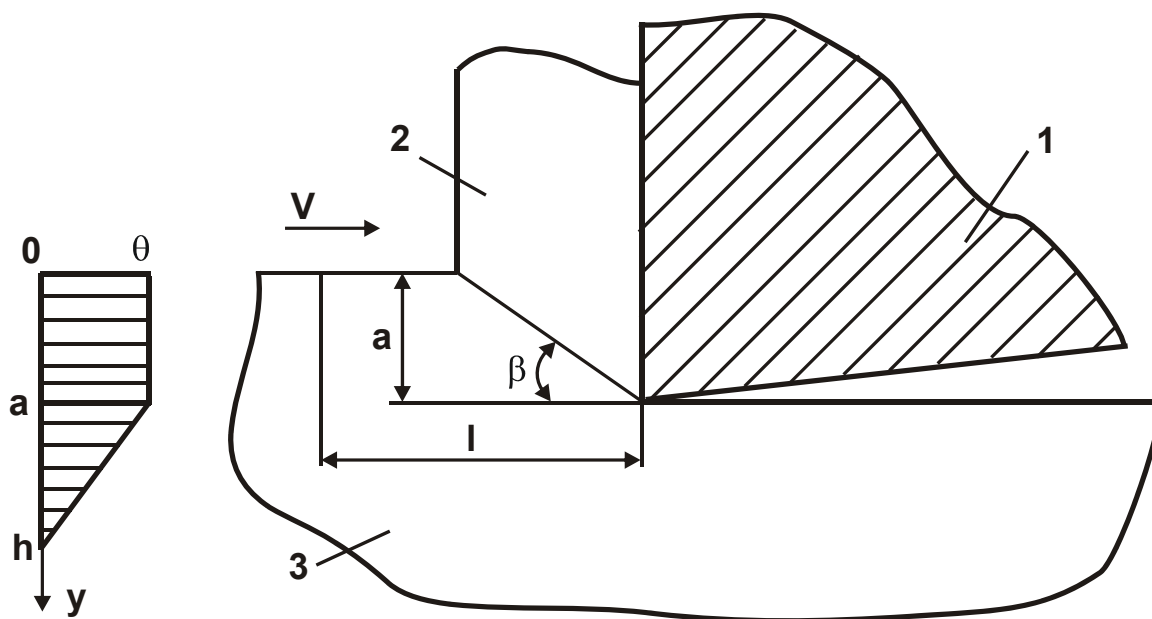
Расчетная схема параметров процесса резания и характер изменения температуры резания θ по глубине нагретого поверхностного слоя обрабатываемой детали h : 1 – резец; 2 – образующаяся стружка; 3 – обрабатываемый материал
